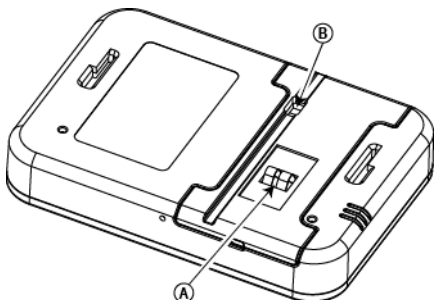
Montagem da Tampa da Bateria (Parte b)
